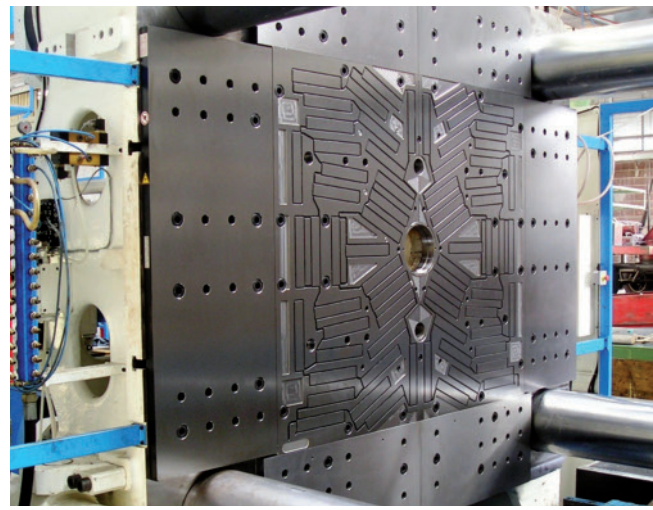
Beispiel einer Pressmag HP-Magnetspannplatte im Einsatz auf einer Spritzgießmaschine mit 16 000 kN Schließkraft
